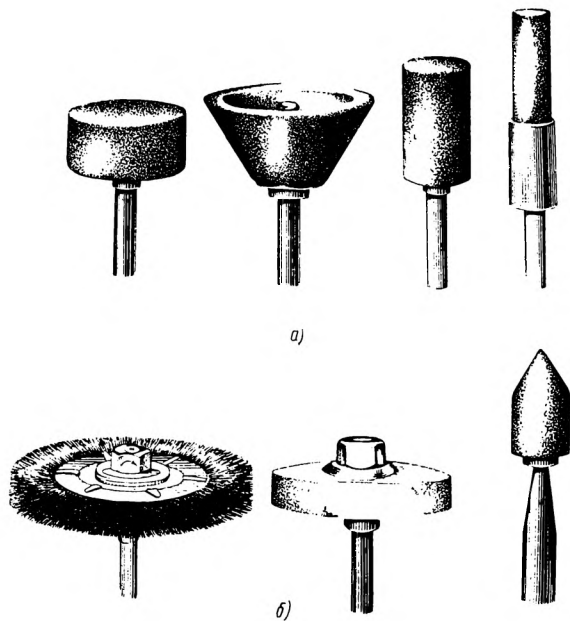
Шлифовальный (а) и полировальный (б) инструмент
